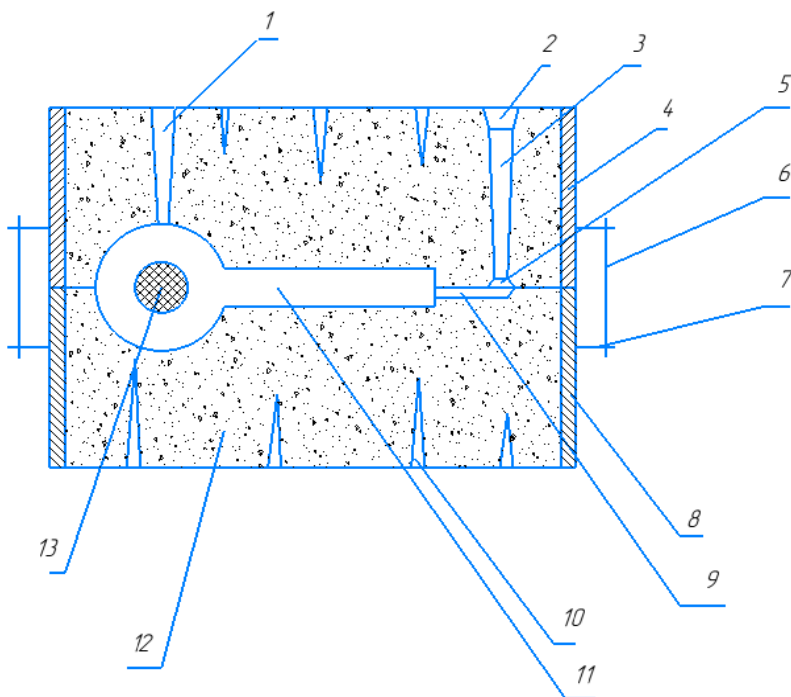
Эскиз литейной формы в сборе для формовки детали «тяга» с горизонтальным расположением стержня (вариант разъема модели и формы № 2)
